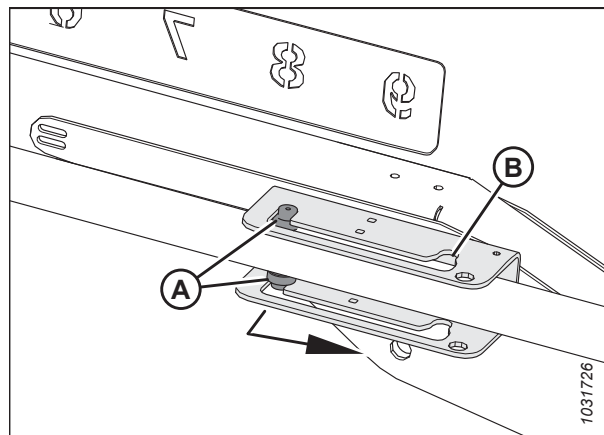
Réglage des vérins avant-arrière de type 2 – Position avant
